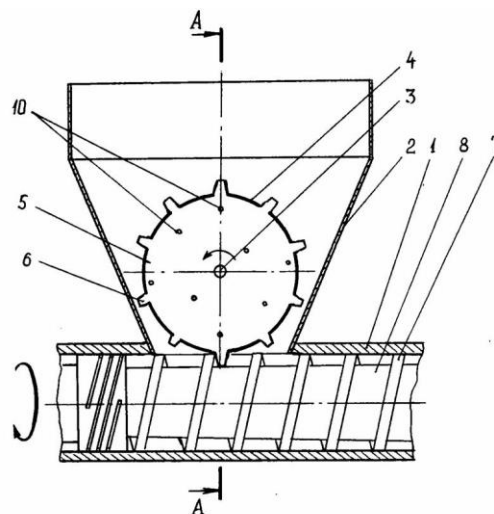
Завантажувальний пристрій черв'ячного екструдера
